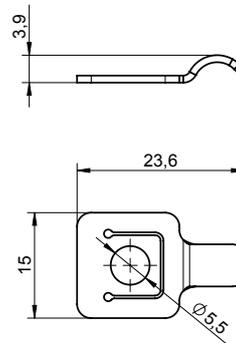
Montagebride für Hardline-Kabel, Typ 1423A1
